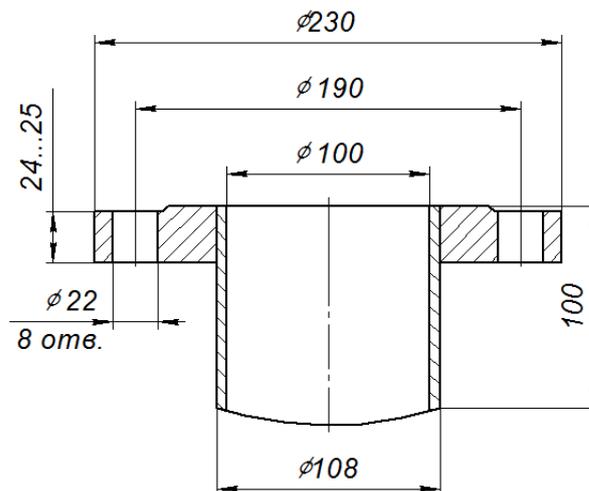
Размеры приварного патрубка на давление 2,5 и 4,0 МПа
